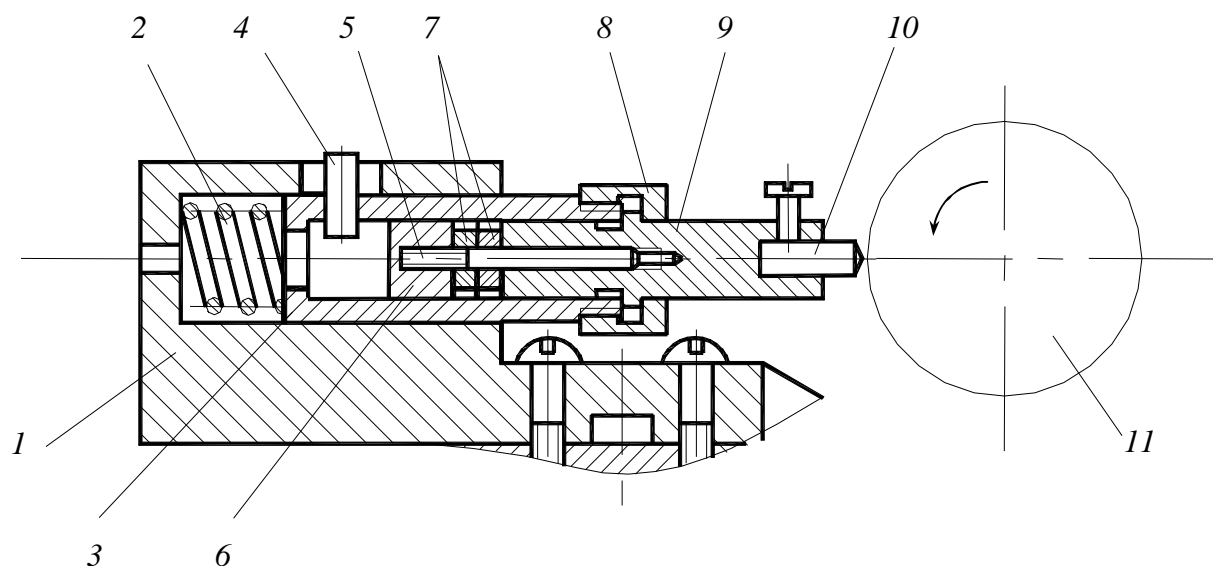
Устройство для алмазного выглаживания заготовок с наложением ультразвуковых колебаний: 1 – корпус; 2 – пружина; 3 – стакан; 4 – штифт; 5 – шпилька; 6 – гайка; 7 – пьезокерамические кольца; 8 – гайка; 9 – волновод; 10 – алмазный выглаживатель; 11 – заготовка
